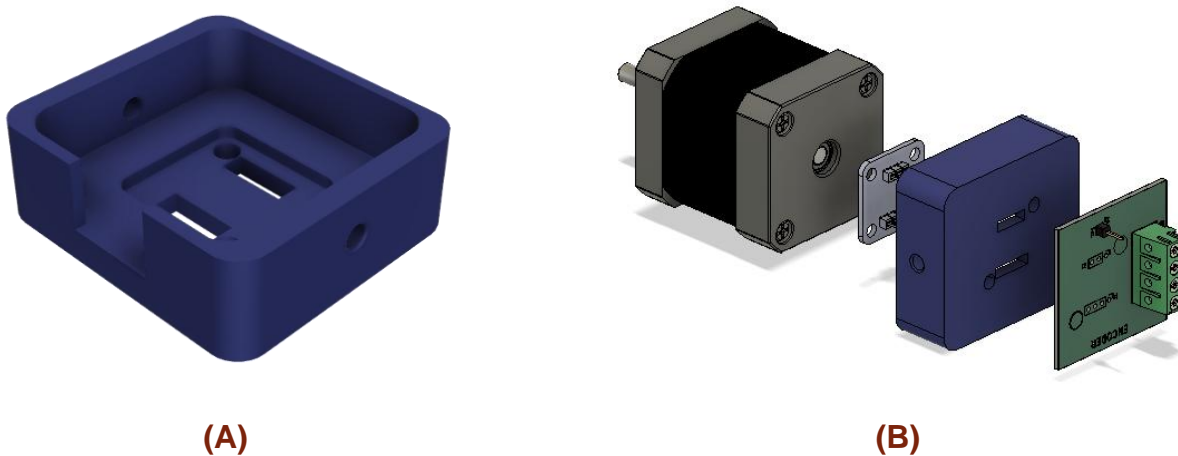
Tapa del motor PaP que alberga el codificador as5600; (A) tapa del motor PaP, (B) ensamble con codificador As5600, motor PaP y tarjeta para interconexión.
